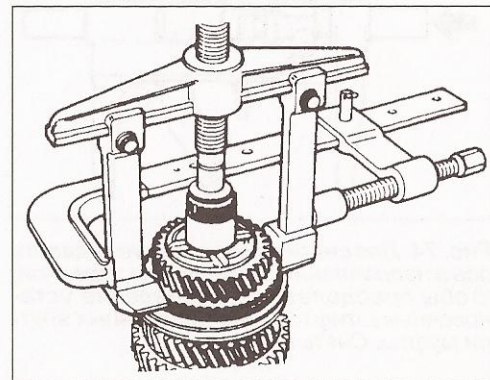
Снятие шестерни 3-й передачи с вторичного вала.
